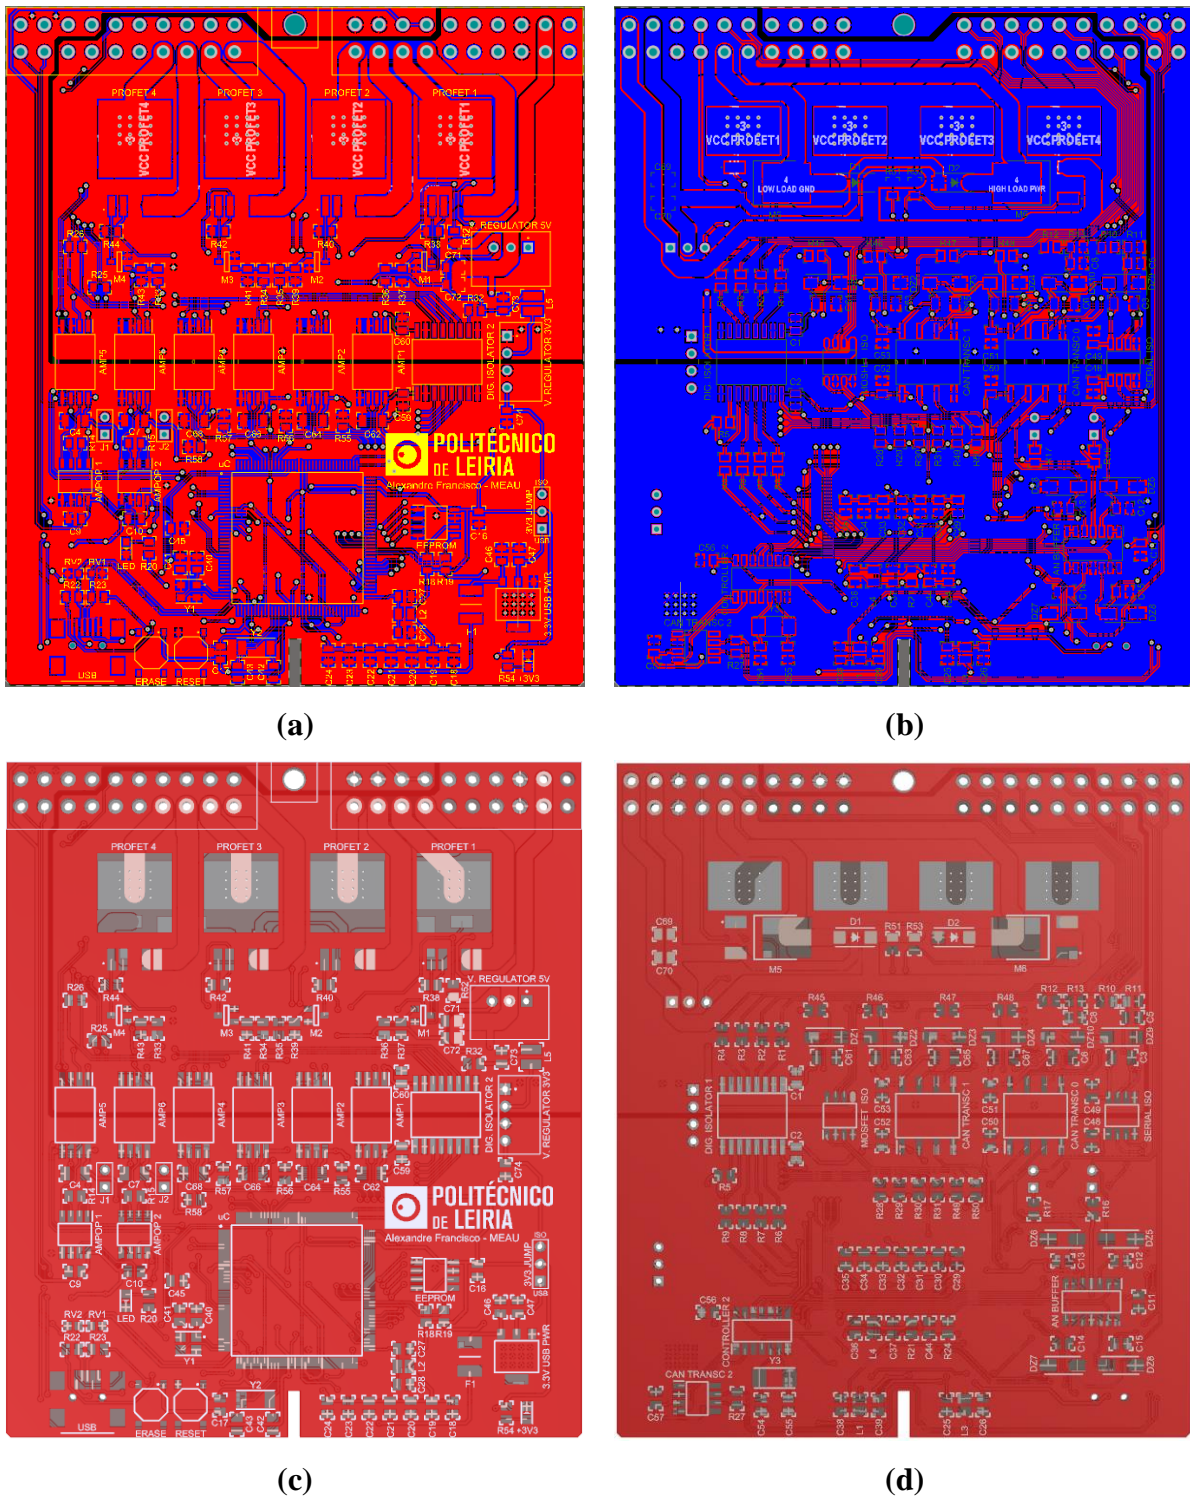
(a) Vista 2D superior da PCB; (b) Vista 2D inferior da PCB; (c) Vista 3D superior da PCB; (d) Vista 3D inferior da PCB.
